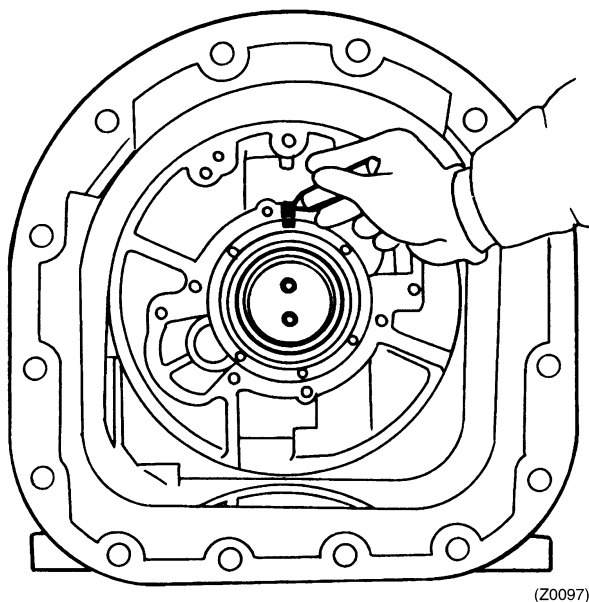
Выполнение отметок совмещения на корпусе и главном держателе подшипников
